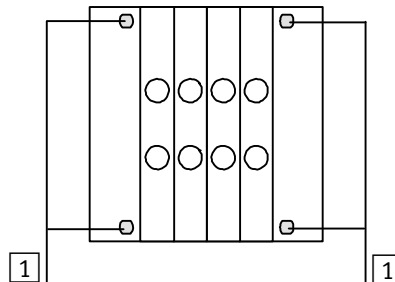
/4: Befestigungsbohrungen für die Fußmontage
